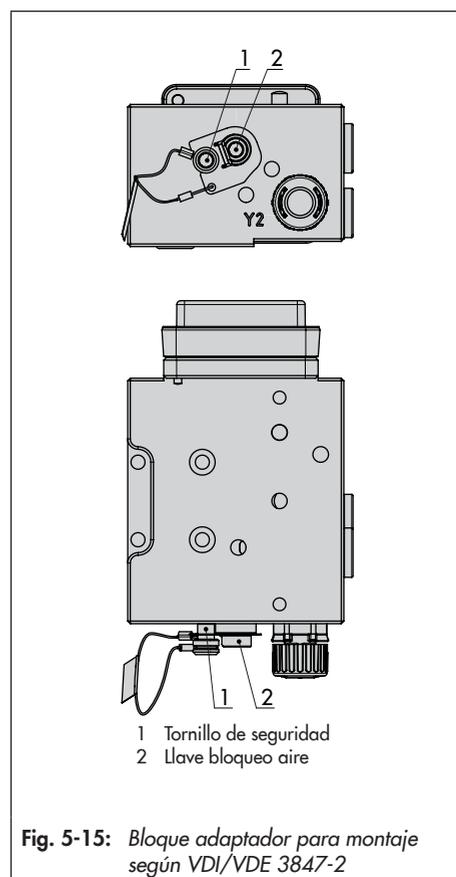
Bloque adaptador para montaje según VDI/VDE 3847-2
